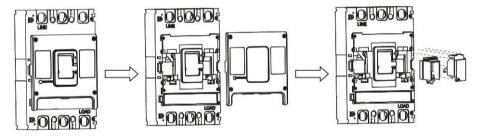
Схема установки аксессуаров внутрь корпуса аппарата
